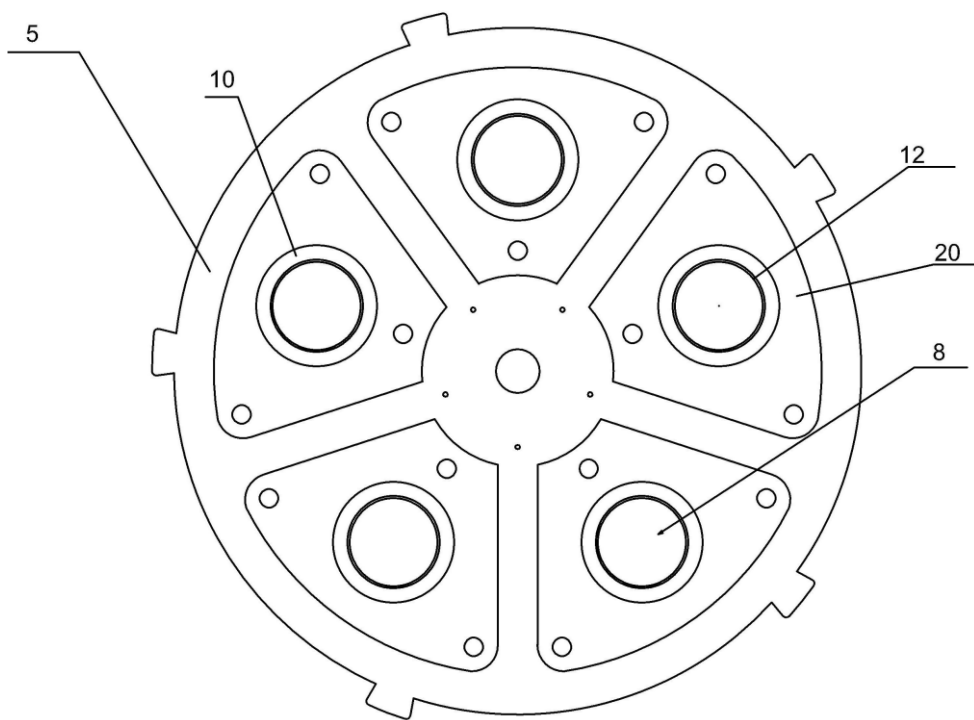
Вид сверху на сменный диск с отверстиями для изделий с ячейками с кольцевыми профилями опорных плит
